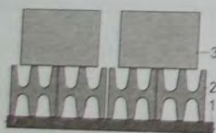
Схема упаковки коробов в печь на профилированные кирпичи: 1 — подина печи; 2 — огнеупорный кирпич; 3 — короб с упакованными стержнями
